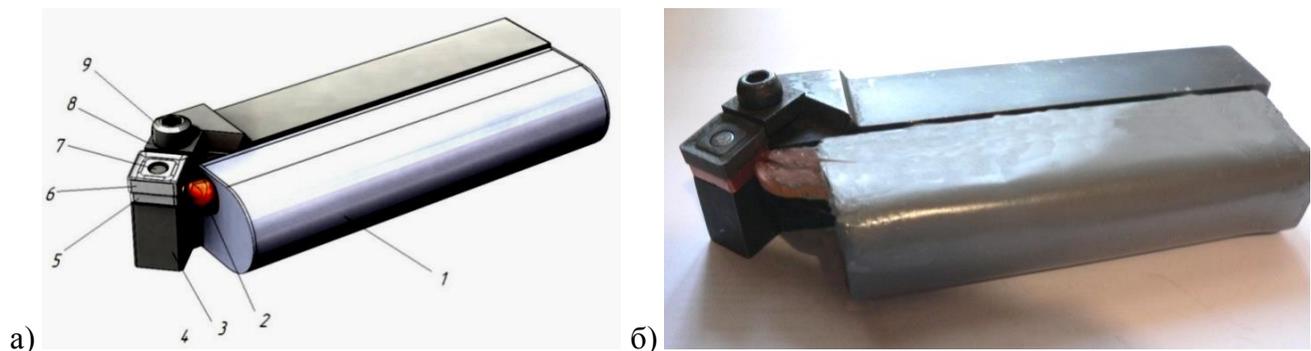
а) – резец с модулем охлаждения (1 – контейнер с плавящимся веществом; 2 – тепловая труба; 3 – державка); б) – фотография резца с модулем
